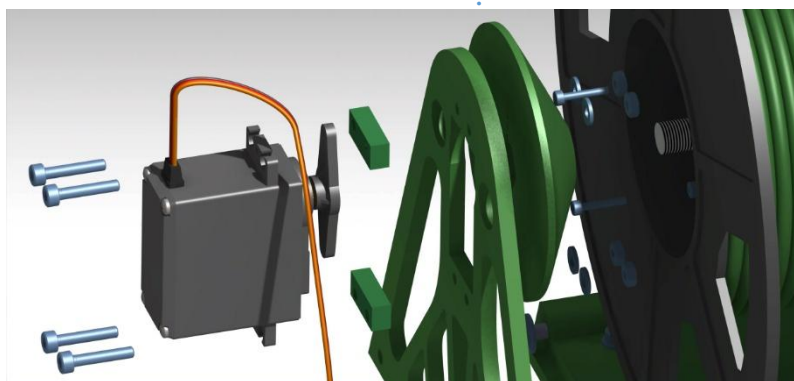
Ensamble del servomotor que acciona la bobina de filamento a través del cono.
